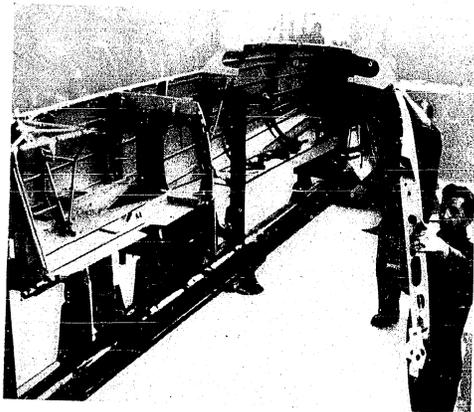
Grundgerüst einer Tragflächenbauvorrichtung nach dem „Baukastensystem“. Ortsbeweglichkeit durch Spindelfüße
